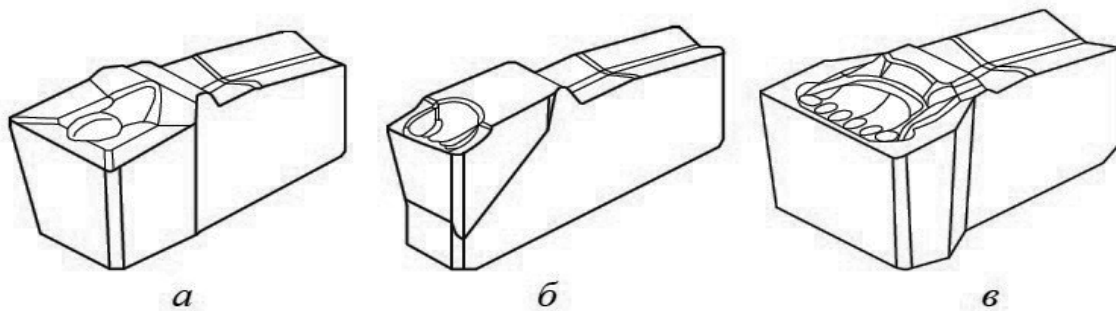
Геометрія пластин: а – 4G; б – 5G; в – 6G
